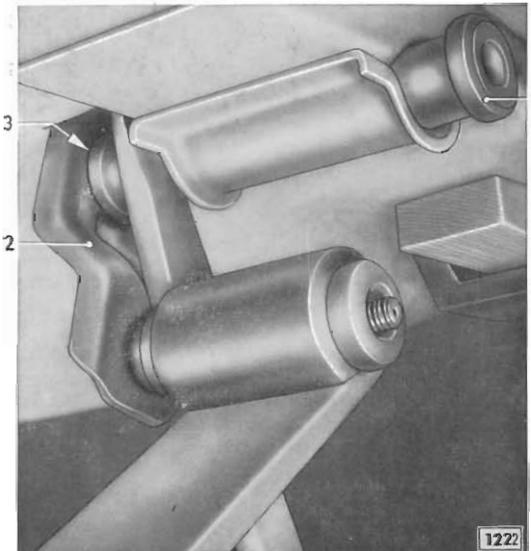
An linker hinterer Federaufhängung Lasche mit Gehängebolzen etwa zur Hälfte aus Aufnahme im Rahmenlängsträger und Federauge herauszwängen
